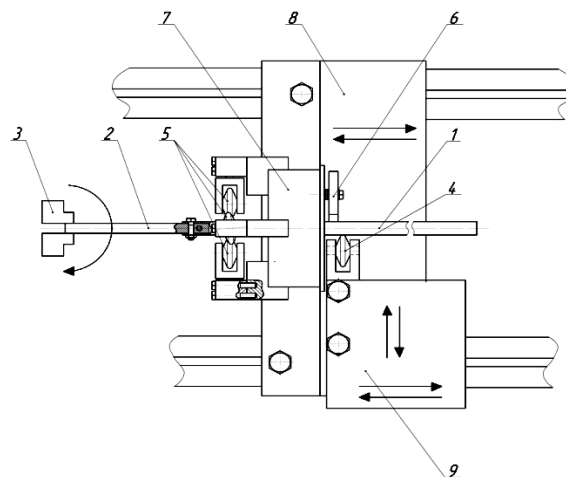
Схема работы установки: 1 – труба – заготовка, 2 – стержень-удлинитель, 3 – патрон, 4 – однороlikовая обкатная головка, 5 – ролики, 6 – упор, 7 – трехроlikовая обкатная головка, 8 – суппорт станка, 9 – резцедержатель
